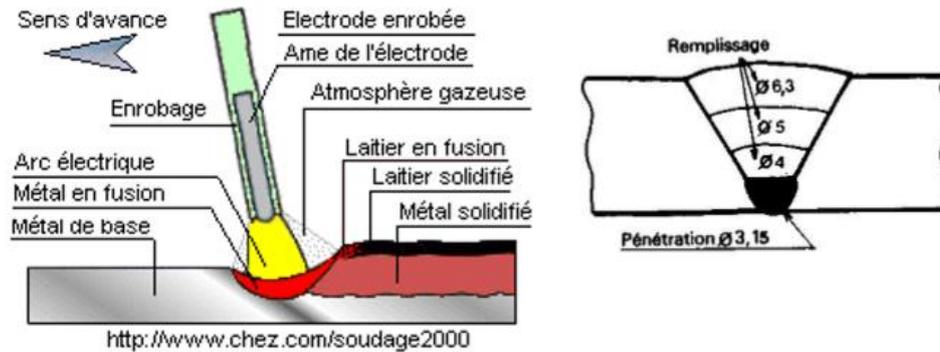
Soudage l'arc électrique avec électrode enrobe
